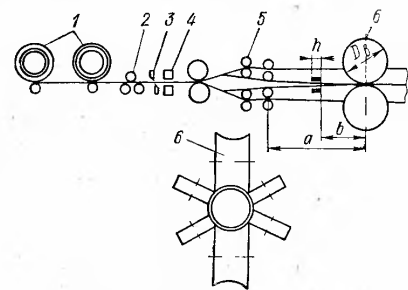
Агрегат для сварки труб из двух лент:
